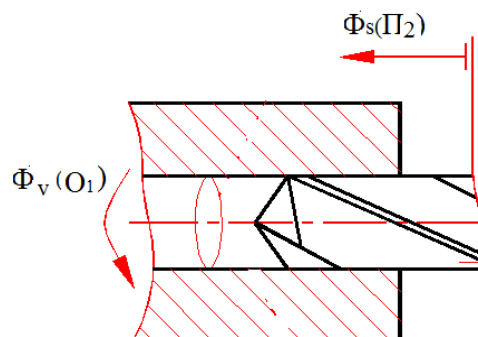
Формоутворюючі рухи при свердлінні та обробці іншим осевим інструментом
